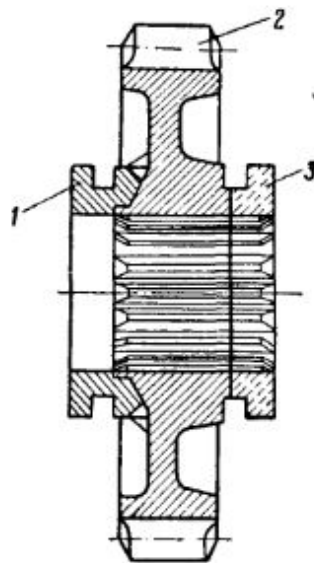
Ремонт зубчатого колеса способом перевертывания
